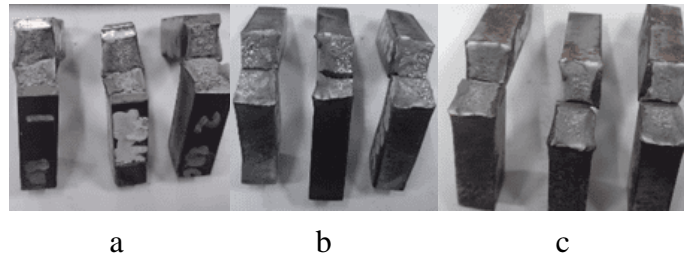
patahan spesimen hasil uji impak kodifikasi 70C. (a.) *weld metal*, (b) *HAZ cast steel*, (c) *HAZ SM490YA
